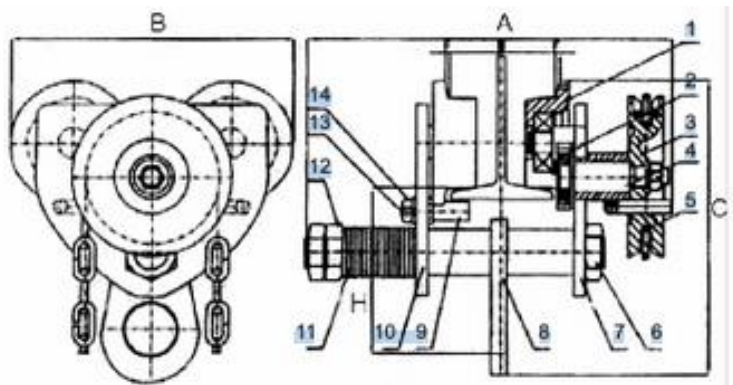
Габаритные размеры тележка приводная для тали серия GCL.
